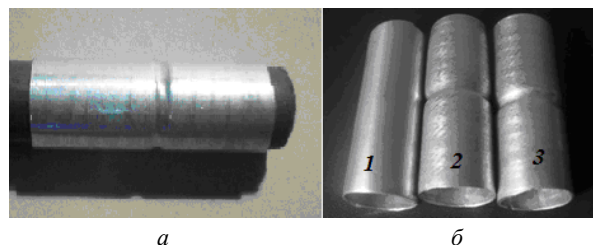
Неразъемное соединение диэлектрического стержня и трубчатой металлической детали (а), заготовка и детали, снятые «срезанными» импульсами (б)
